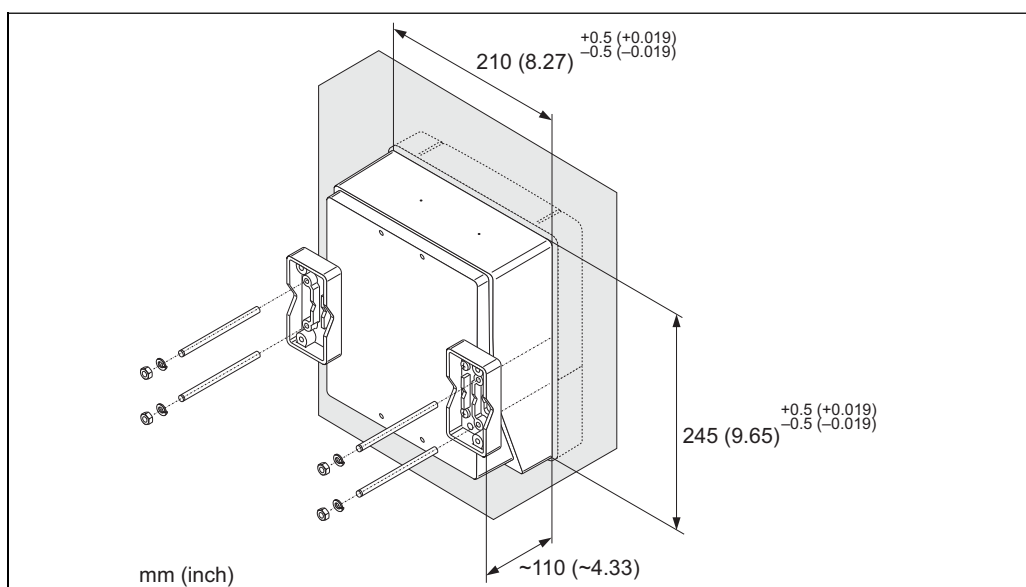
Installation sur panneau (boîtier pour montage mural)
